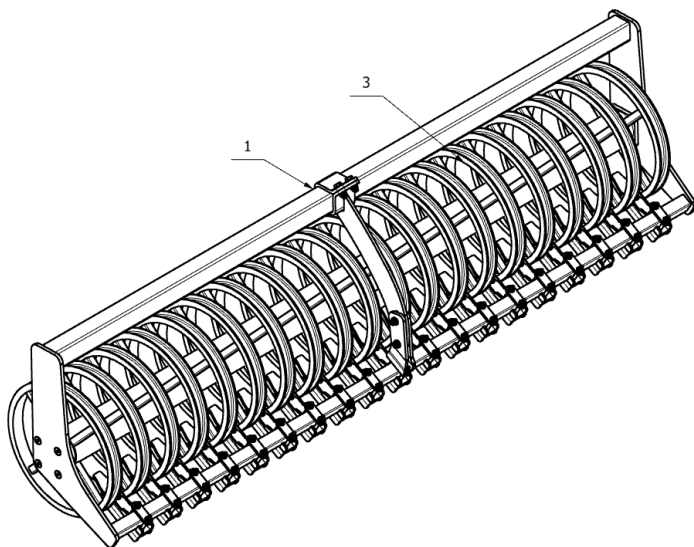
Wał packer $\varnothing 510\text{mm}$ – mocowanie skrobaka do belki.
